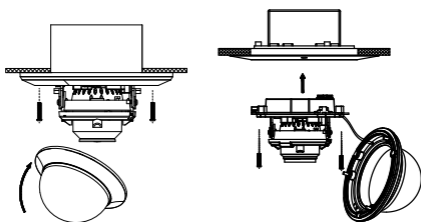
Закрепление камеры (Слева) Камера II типа
